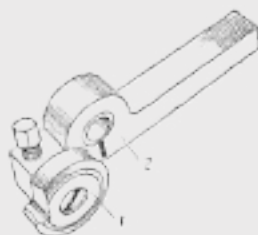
Кріплення круглого фасонного різця у пружній державці: 1 — круглий фасонний різець; 2 — пружна державка
